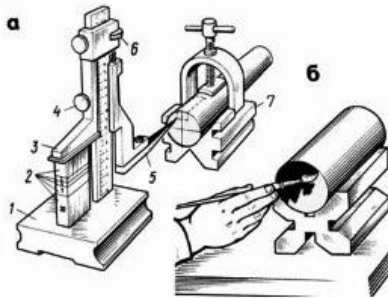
Розмічання шпонкової канавки на валу: а - розмічання шпонкової канавки на пристрої; б – нанесення на торець валика розчину мідного купоросу;
